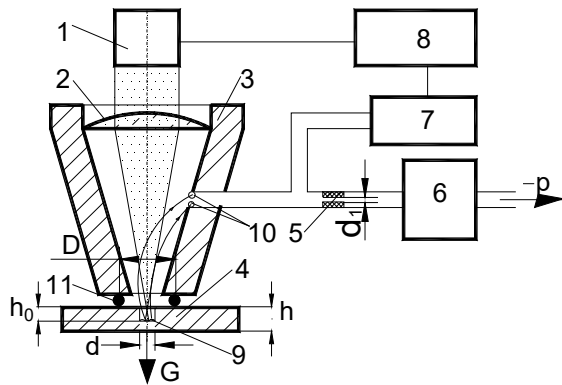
Схема пристрою для обробки глибоких мікроотворів (лунок) з вакуумним видаленням продуктів ерозії з їх порожнини: 1 – лазер, 2 – лінза, 3 – корпус лінзи, 4 – заготівка, 5 – дросель, 6 – вакуум насос, 7 – вакуумметр, 8 – блок живлення лазера, 9 – розплав на дні лунки, що обробляється, 10 – продукти лазерної ерозії матеріалу заготовки
